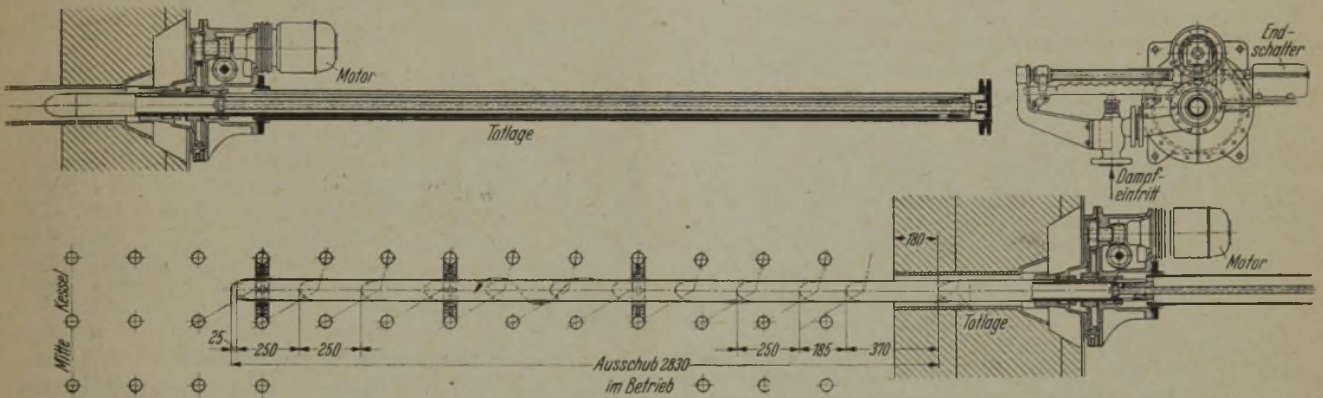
Langvorschubbläser zur Reinigung des ersten Kesselzuges. Werkzeugnung Ver. Kesselwerke AG., Düsseldorf.
